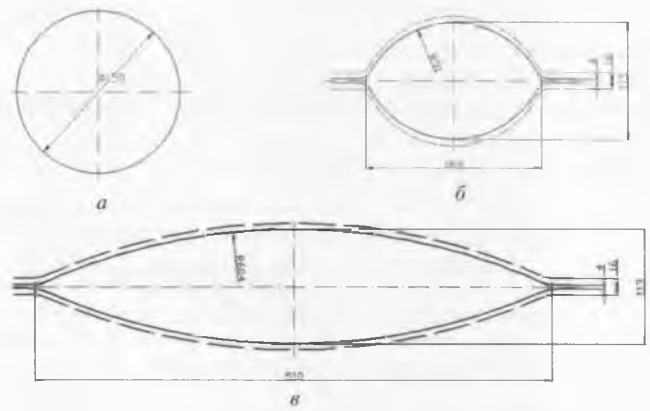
Вид заготовки (а) и инструмента (б, в) для моделирования прокатки круглой заготовки в овальном калибре
